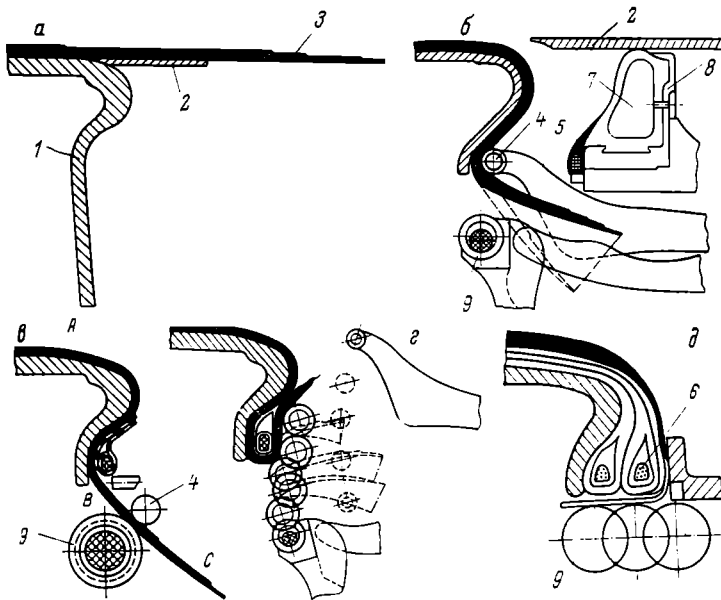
Схема сборки покрывки на станке АД-ИЗ:
